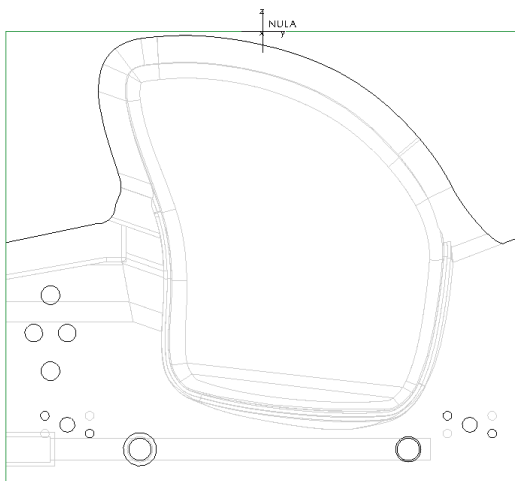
Definice souřadného systému pro 5-ti osé obrábění
